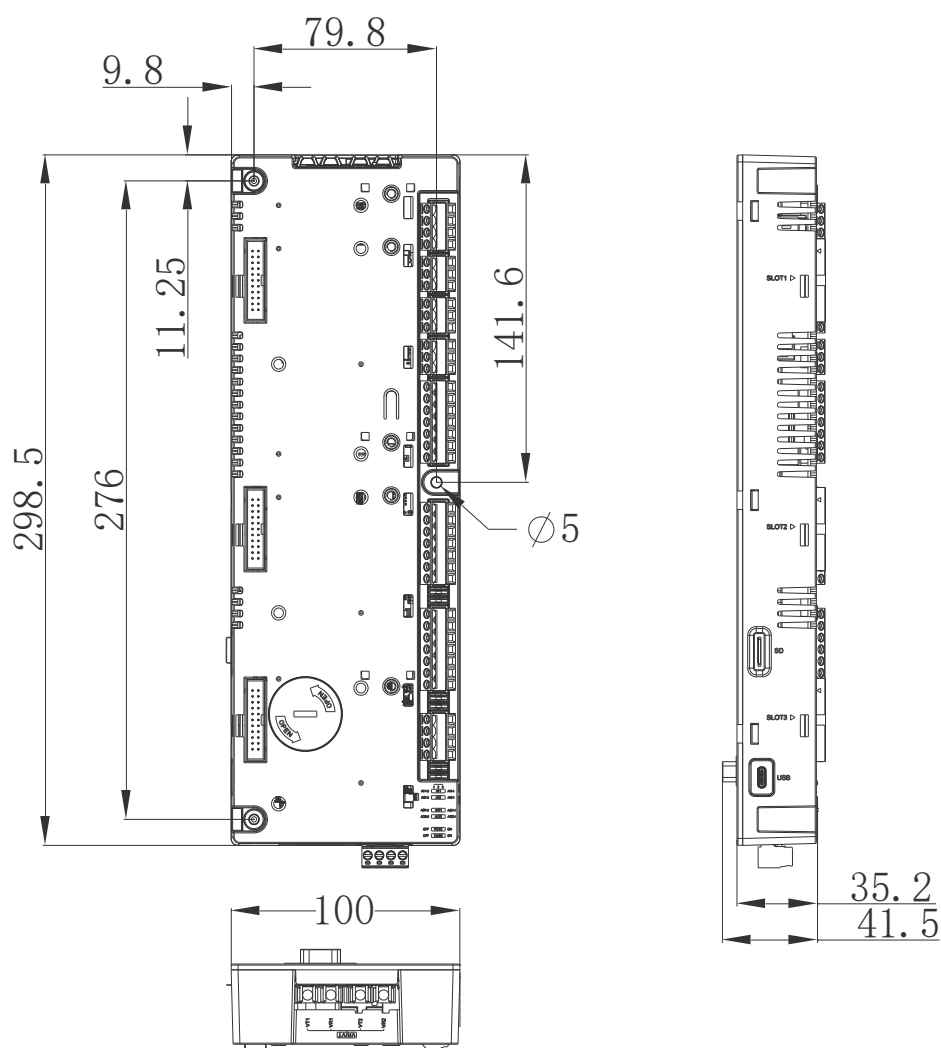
Габаритный чертеж модуля управления (мм)
